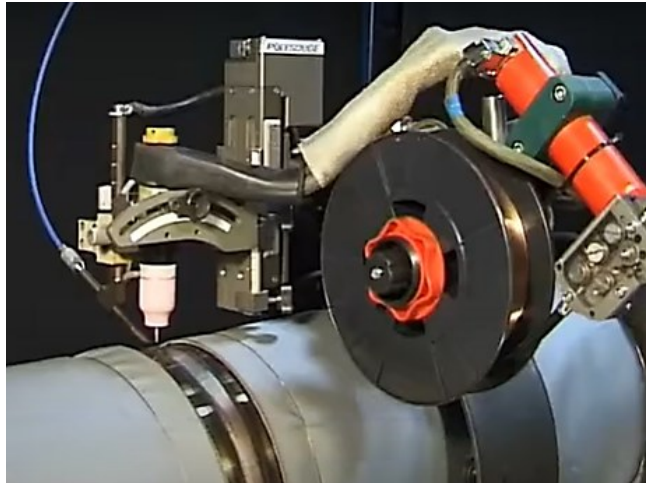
Manipulador mecânico para o processo GTAW alimentado. Fonte: [8]. Disponível em: <<https://www.polysoude.com/orbital-and-automated-welding/automated-welding/>>
